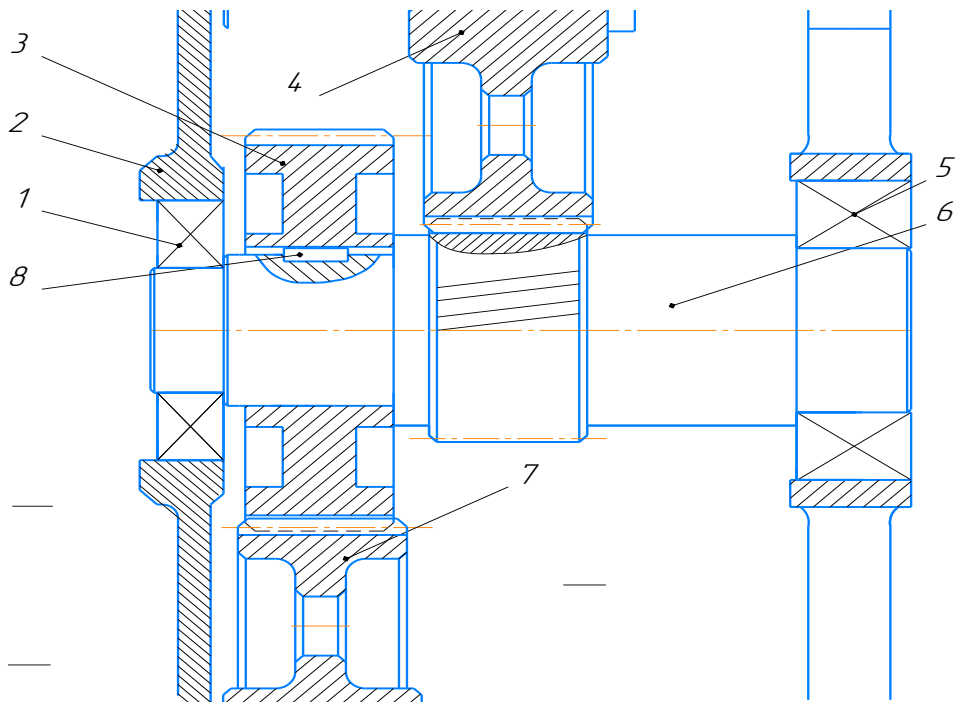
Ескіз вузла редуктора ТСН.02.102
